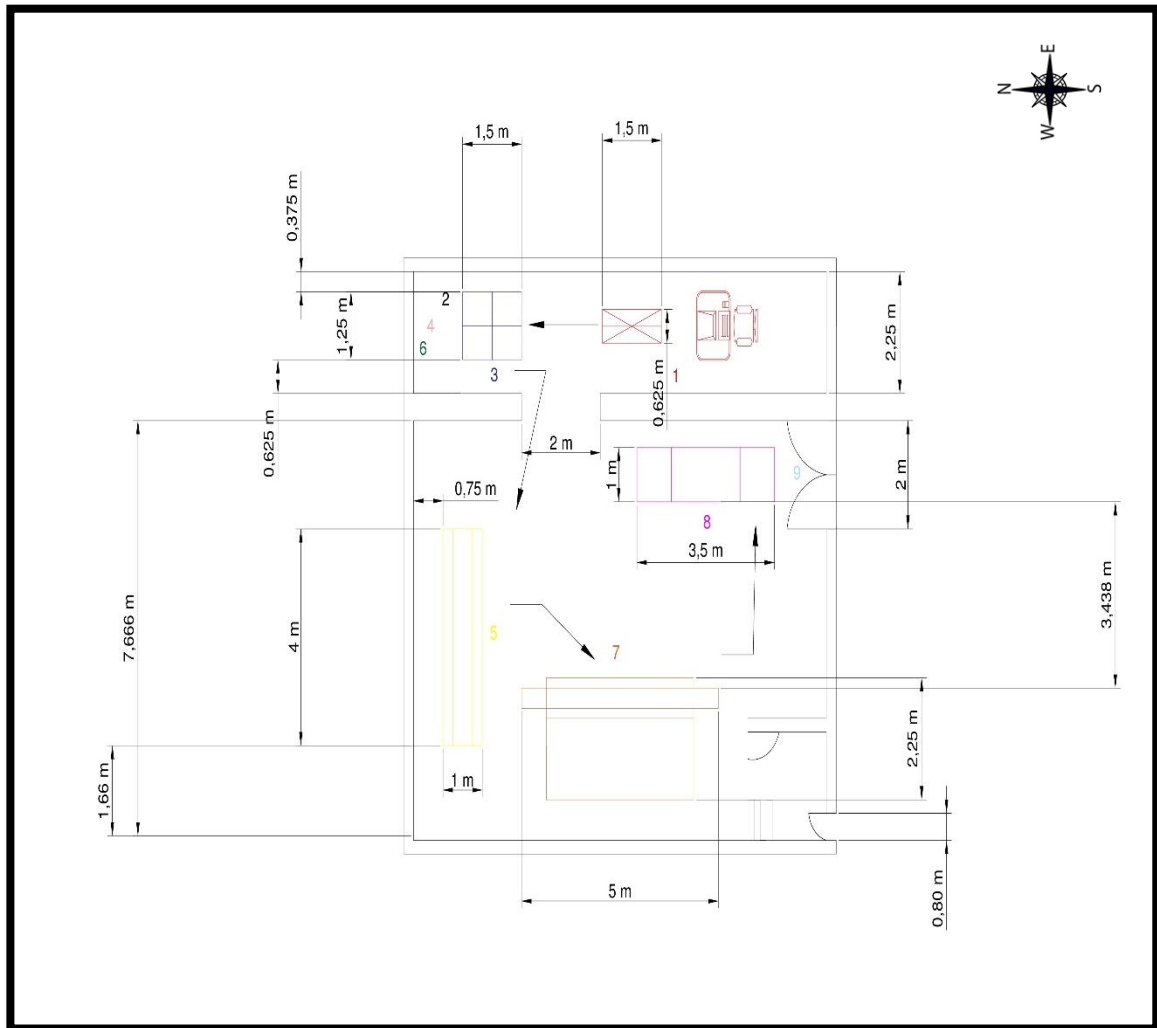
Fuente propia (2017). Layout propuesto para FORTECMA.
